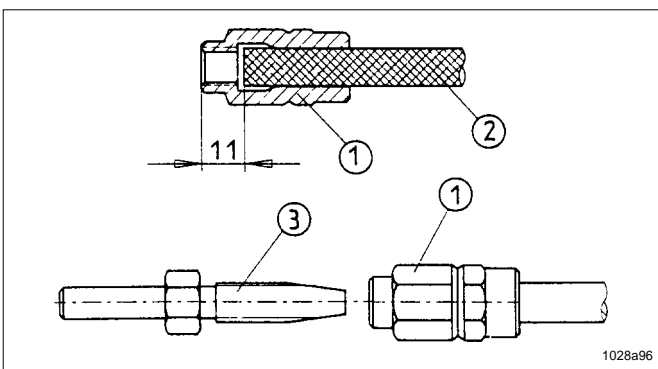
Prémontage des douilles filetées et des embouts pour tuyau sur la conduite principale
